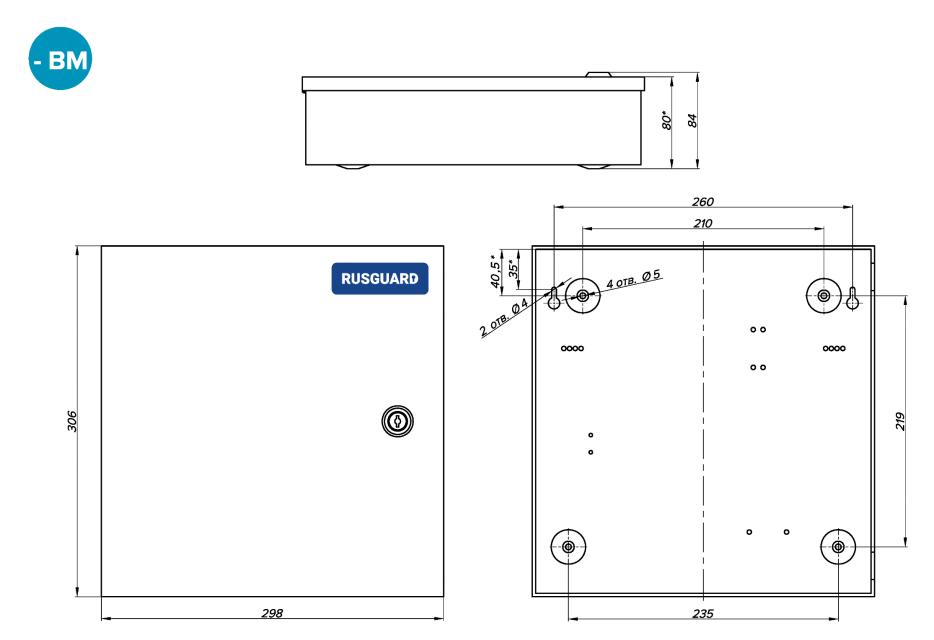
Габаритные размеры и крепеж контроллера в корпусе исполнения -ВМ
